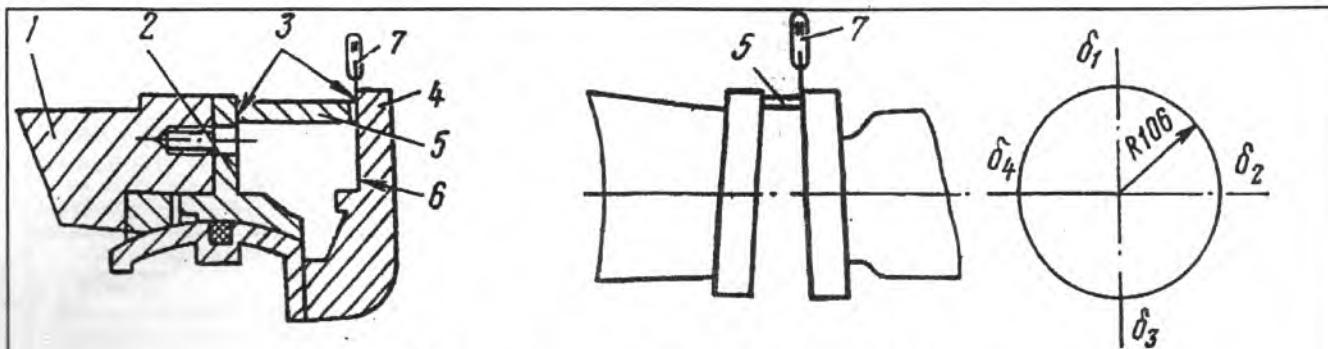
Схема замера соосности вала двигателя с валом главного редуктора калибром:
